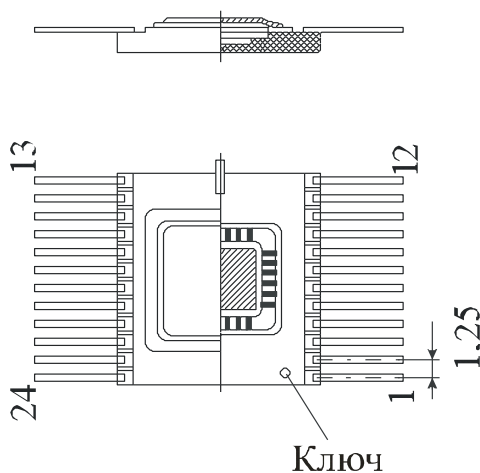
Конструкція металокерамічного корпусу 4118
